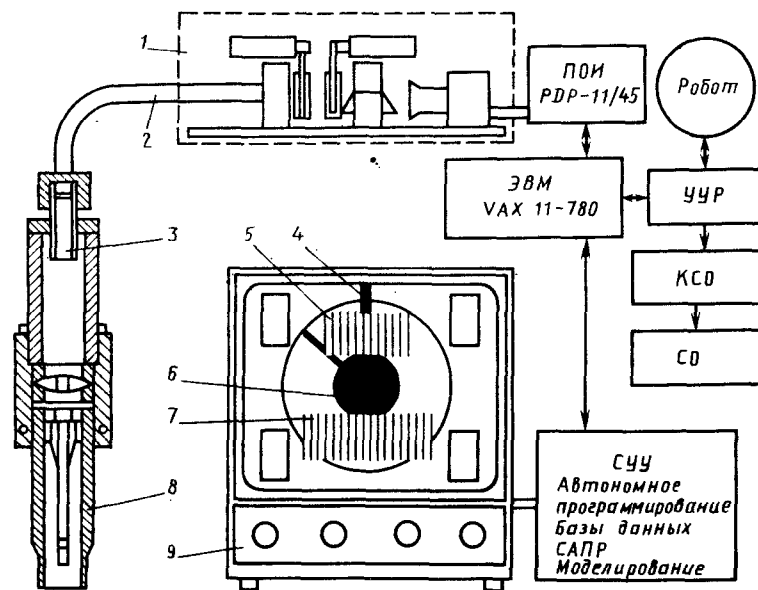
Схема включения СТЗ в адаптивный роботизированный комплекс для сварки двигателя космического корабля «Шатл»:
